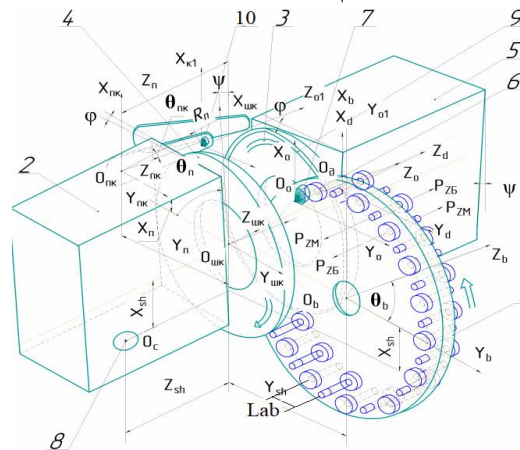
Розрахункова схема формоутворення торців деталей різних діаметрів з розташуванням їх у барабані подачі
